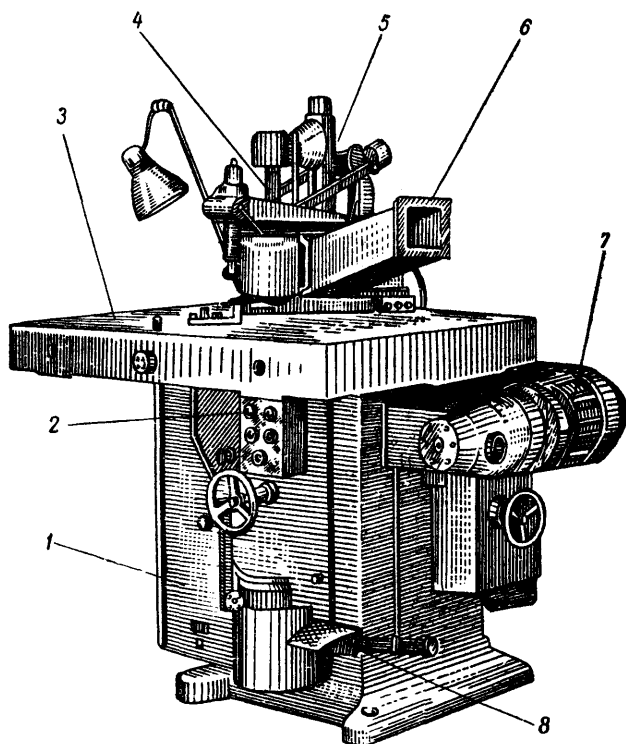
Фрезерный станок с автоматической подачей ФА-4.
